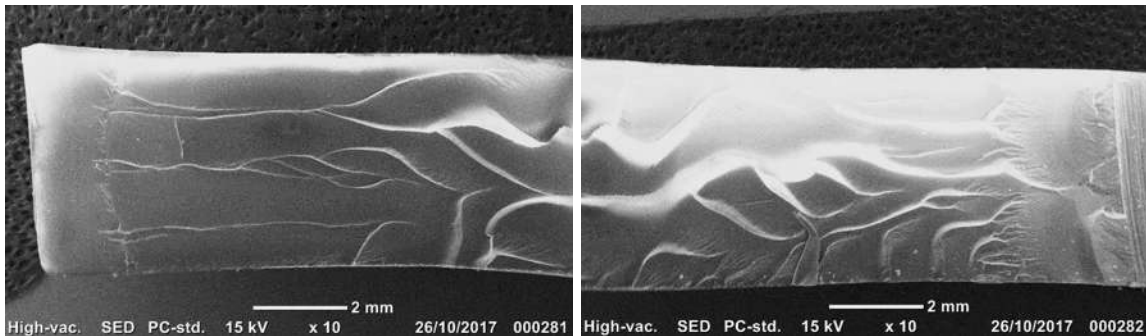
16. Superficie inferior de fisuración en PMMA a 340 µm.
